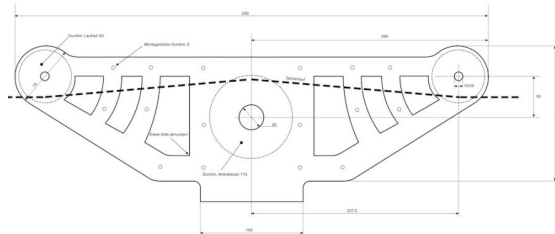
Querschnitt einer elektrisch angetriebenen Seilkamera
